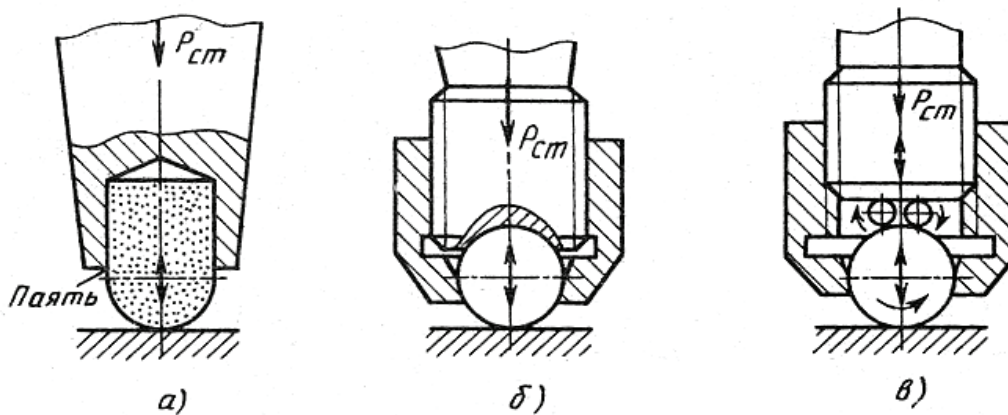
Схема крепления инструмента: а, б — жесткое; в-с обеспечением качения
